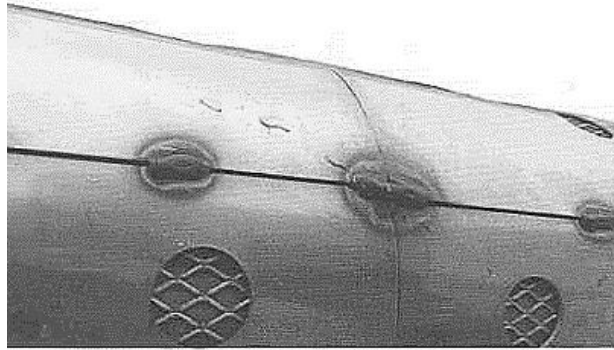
Защитный кожух фильтра с применением сварки, состоящий из листов металла длиной 1 метр
